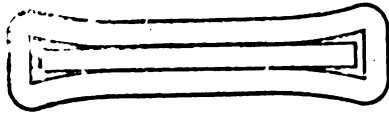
Aspect d'une soudure verre-cuivre sans l'emploi de borax.
